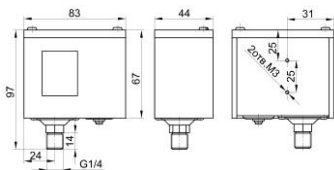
Габаритные и присоединительные размеры РД-2Р-0,8МПа-G1/2 (модель 35)
